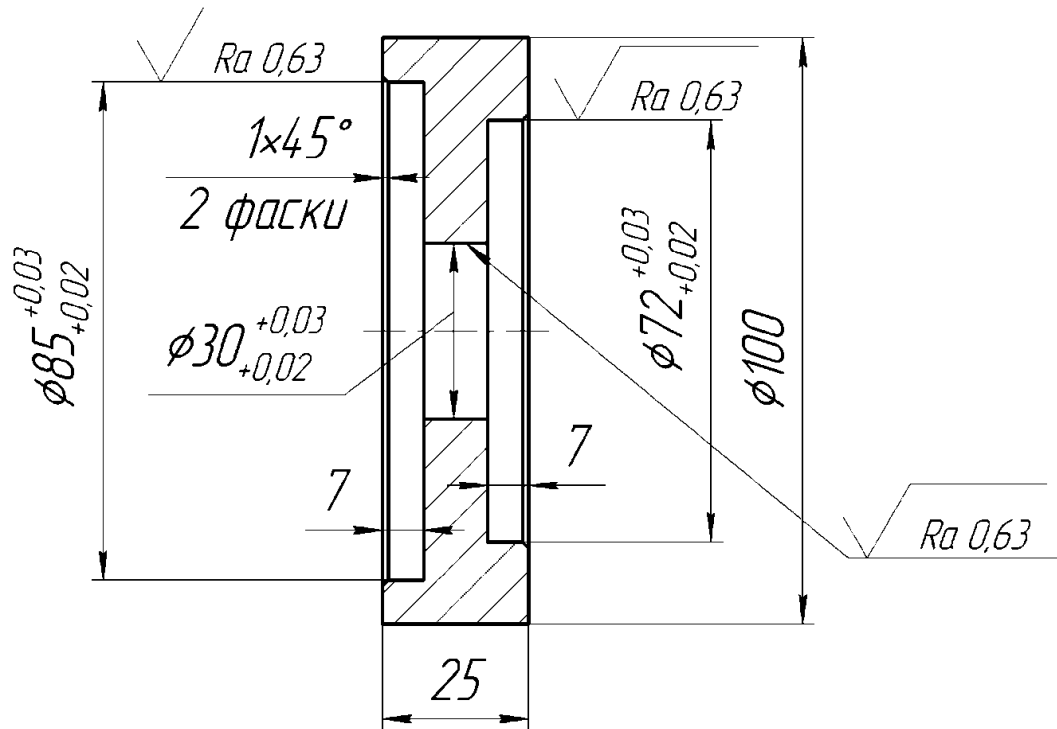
Центрирующее приспособление для сборки клеевого соединения «вал-подшипник»
